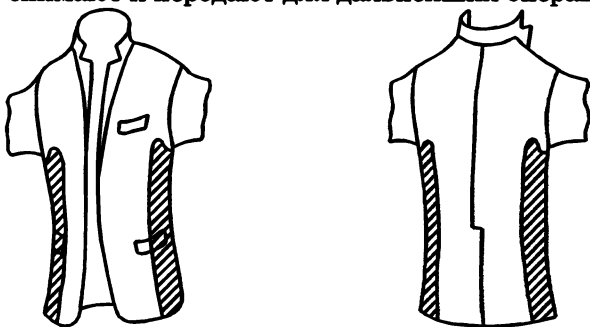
Схема расположения обрабатываемых участков левой и правой боковых частей пиджака
